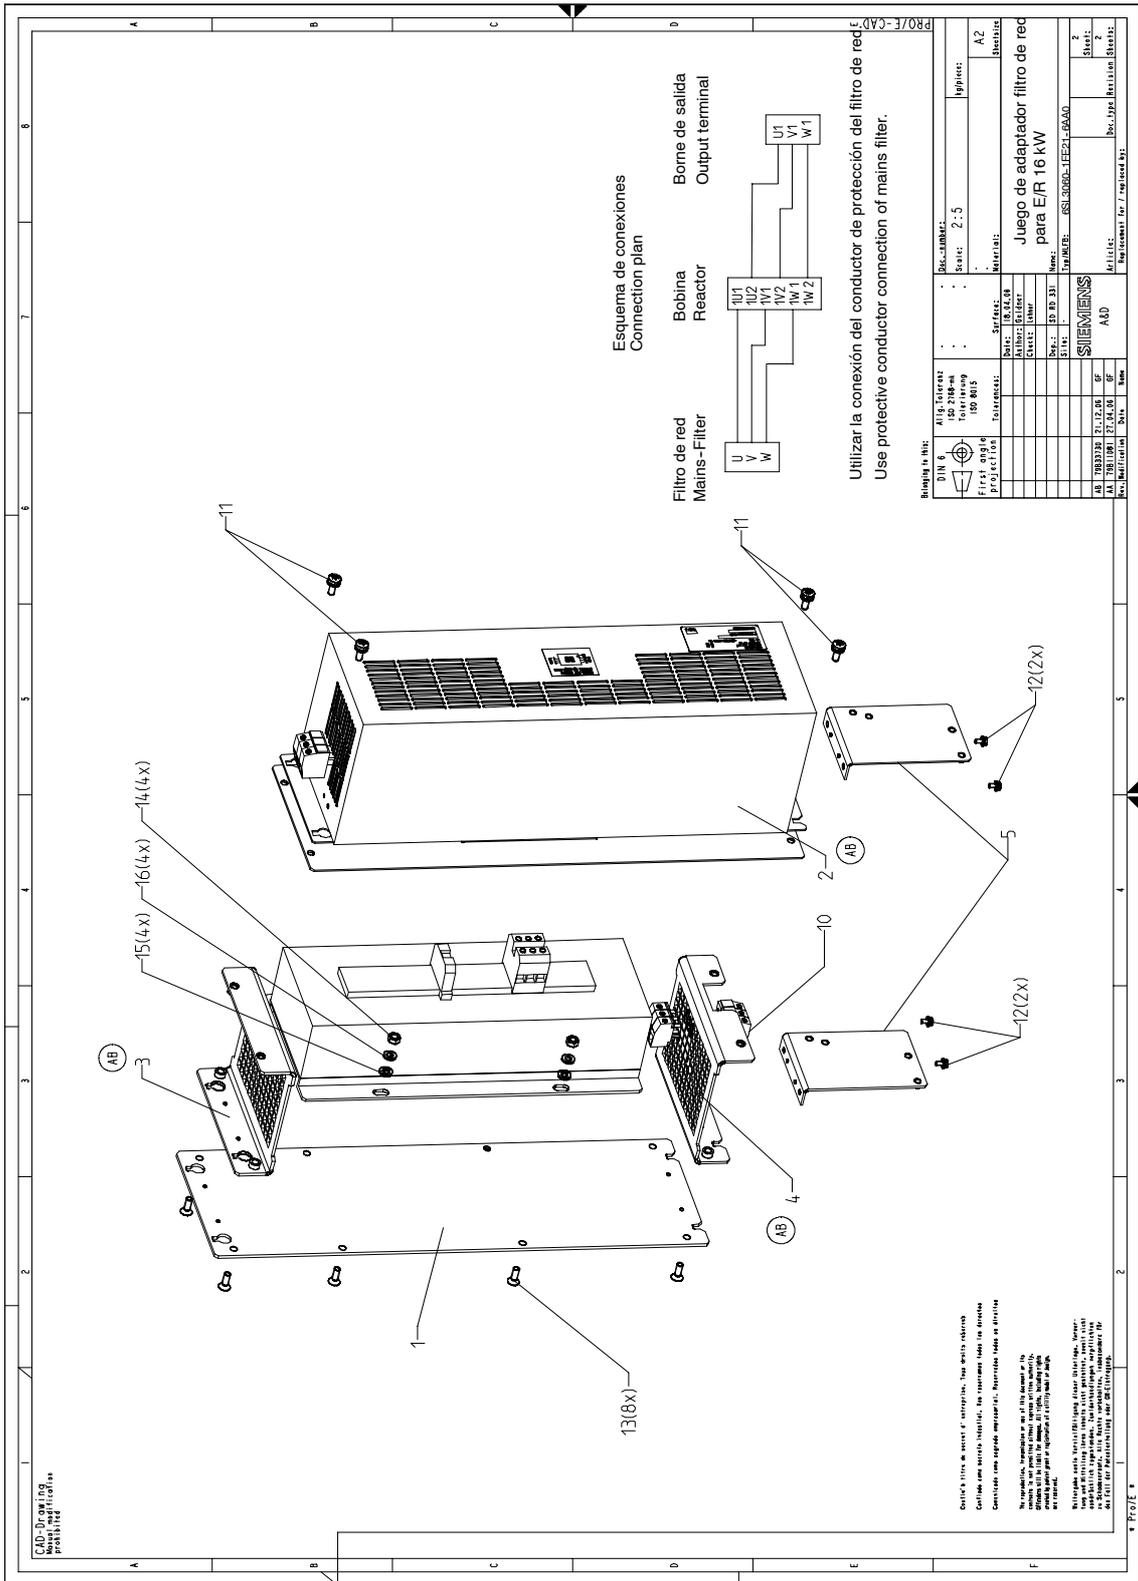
Juego de adaptador filtro de red para módulo E/R 16 kW, 6SL3060-1FE21-6AAx; montaje
